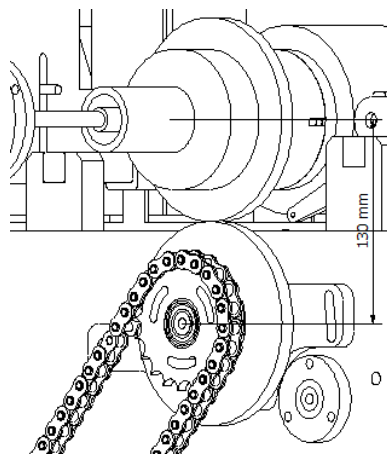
DISTANCIA ENTRE CENTROS DE ENGRANAJES
